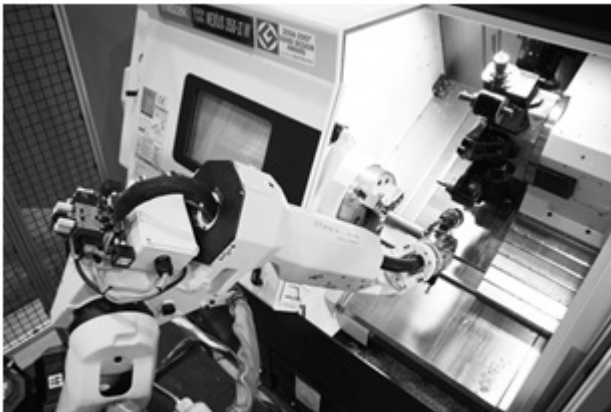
Робот манипулятор устанавливает заготовку в станок
